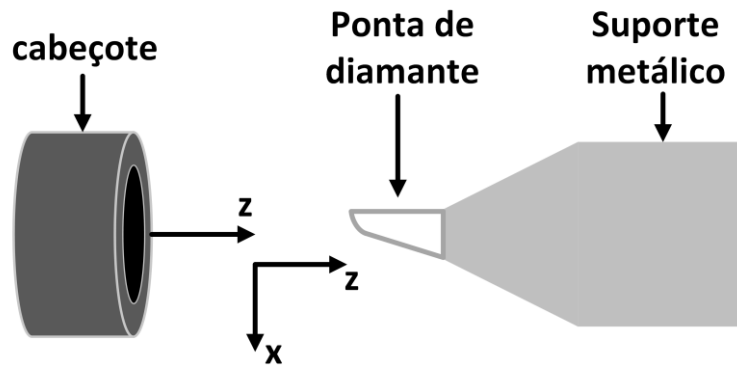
Esquemático dos principais componentes de um torno CNC.
